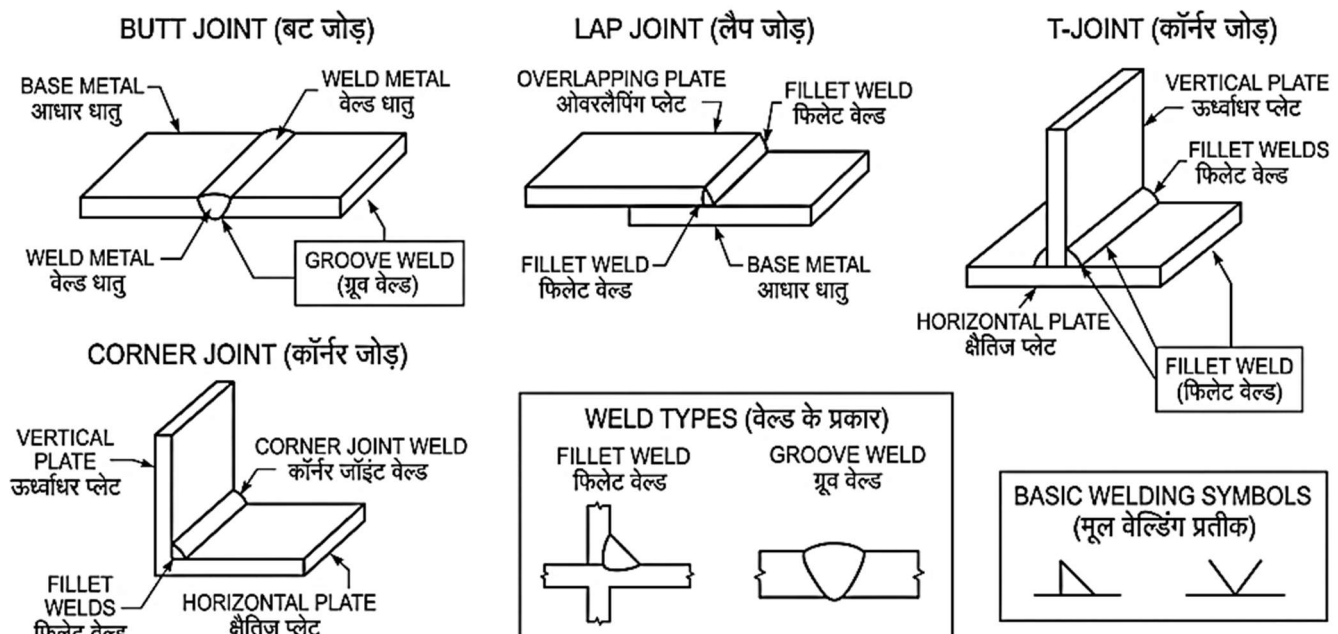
Types of Welding Joints, Weld Types and Basic Welding Symbols | वेल्डिंग जॉइंटों के प्रकार, वेल्ड के प्रकार एवं मूल वेल्डिंग प्रतीक
